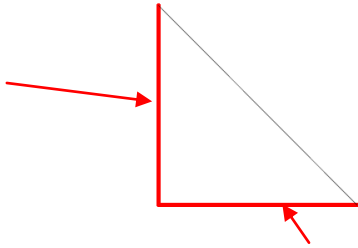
Zonas de soldadura de las cartelas
